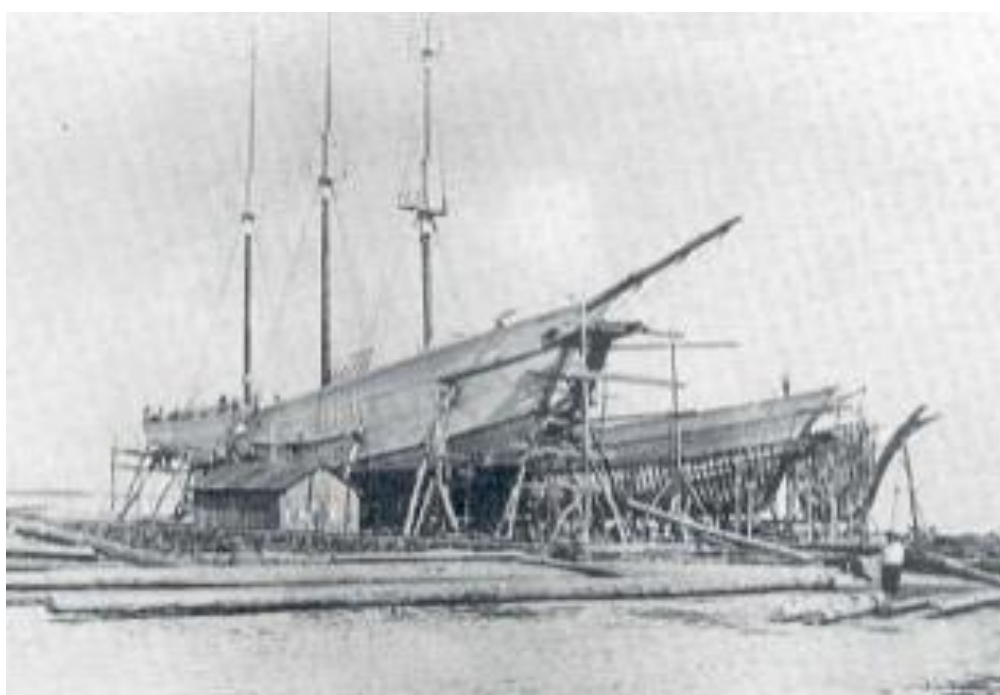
, Construção em Esposende dos lugres de quatro mastros "Esposende I", "Francisco Manoel" e "Troviscal", fotografia de Col. José Figueiras 1918 - 1922, armador Vinagre, Borges & C.^a - pormenor da construção da proa em três fases e a colocação do gurupés.²⁰⁶
